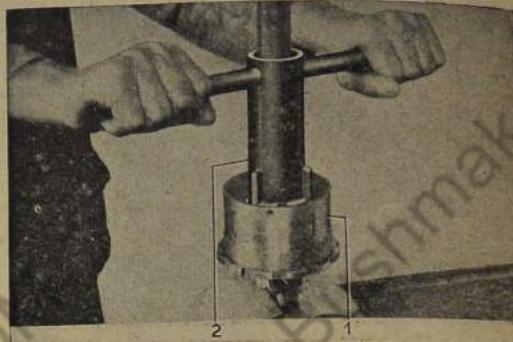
Nutmutter für Schrägkugellager vom Antriebskegelrad abschrauben
